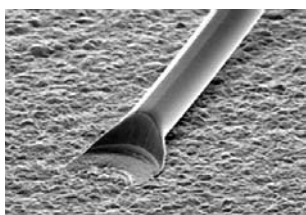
Метод «шарик-клин», вторая точка сварки
